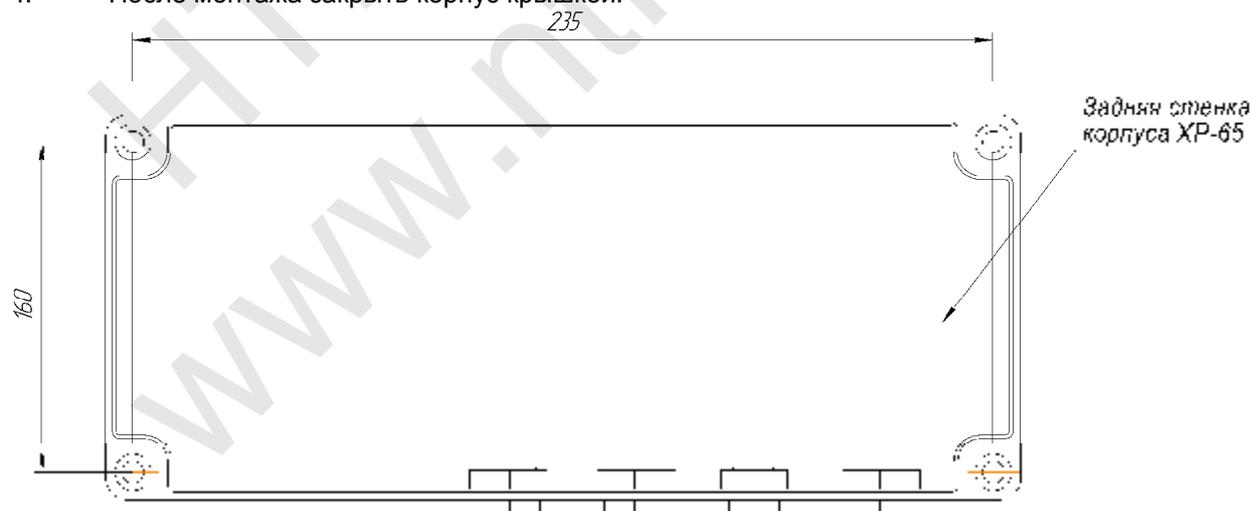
Разметка крепежных отверстий блока XP-65 для крепления на стене.
